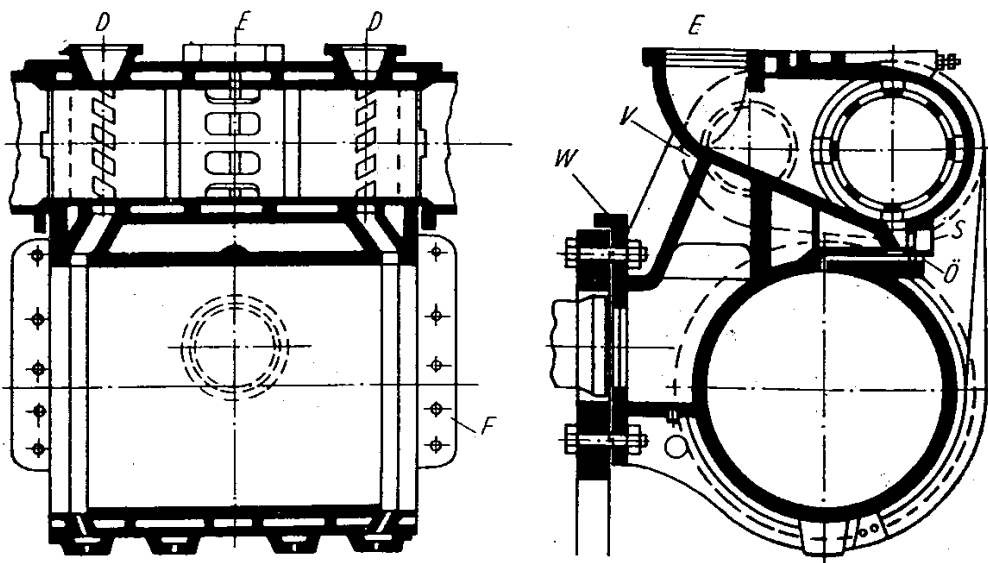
Zylinderblock einer älteren Einheitslokomotive mit Eckventil-Druckausgleichern (siehe auch Bild 48)
